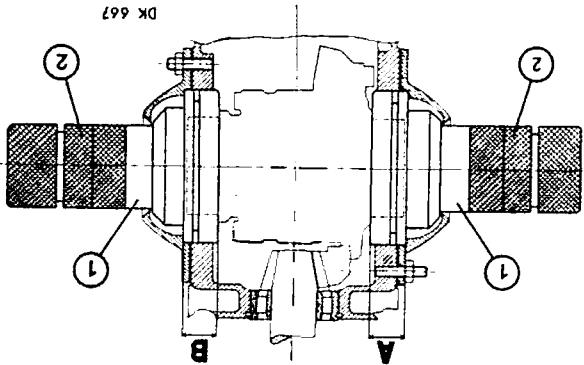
/2 Ermittlung der Einbaumasse für Kegelrollenlager und Ausleichscheiben
